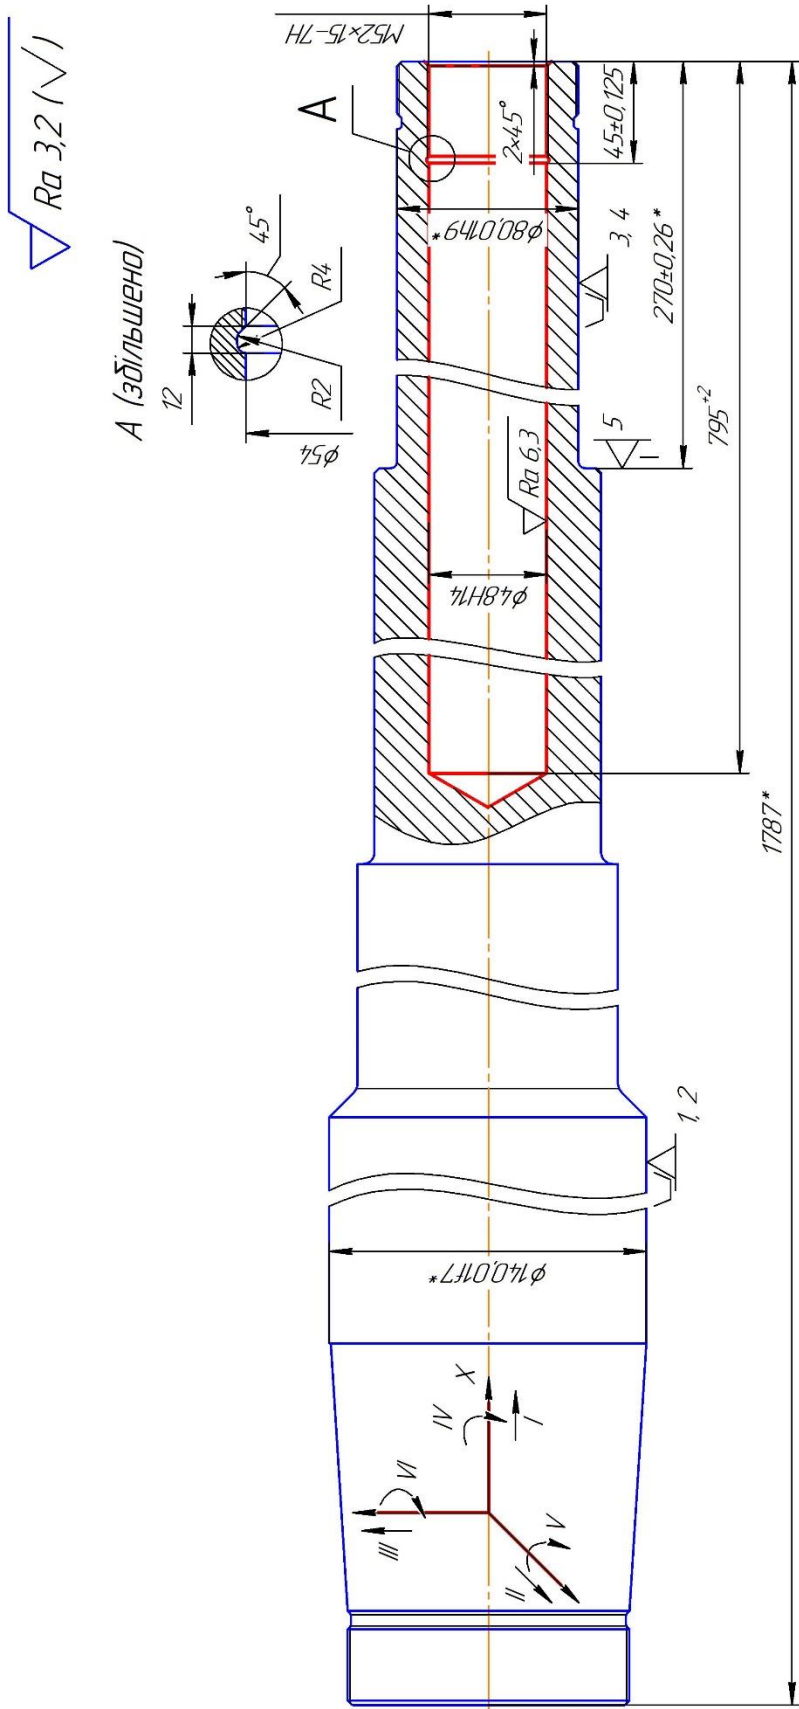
Схема базування заготовки на горизонтально-розточувальній операції
